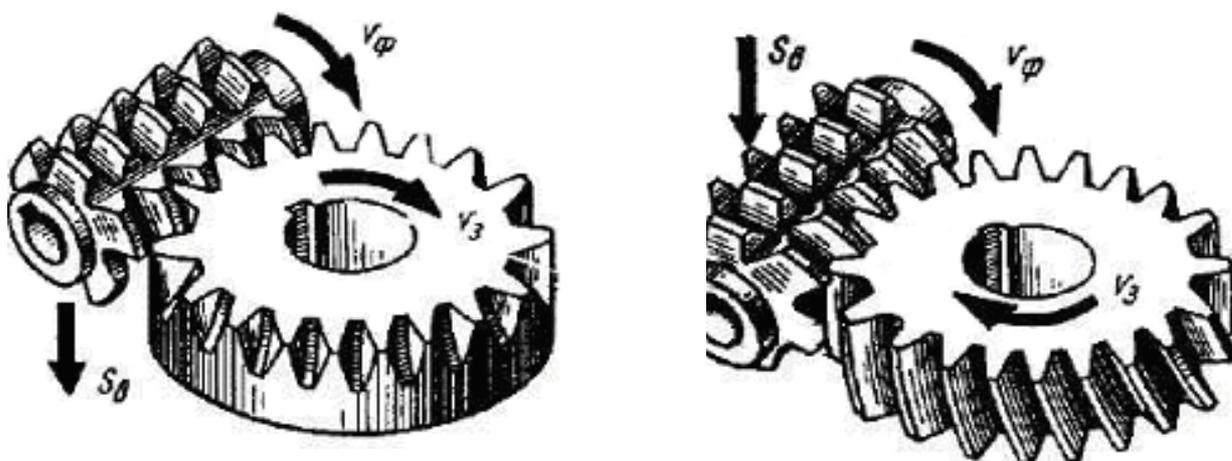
Схема нарезания зубчатых колес червячными фрезами.
